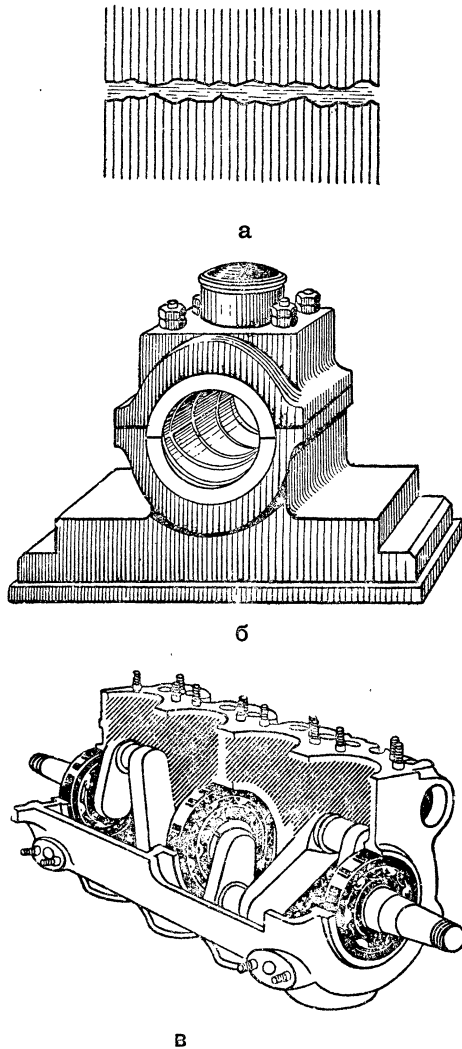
а) смазка между трущимися поверхностями; б) подшипник скольжения; в) коленчатый вал двигателя на шариковых подшипниках.
